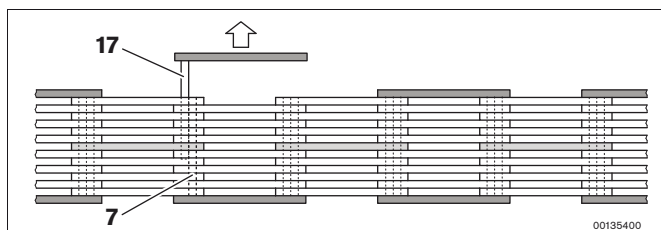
Удалить коренную цапфу с соединенной с ней сварочной пластиной
